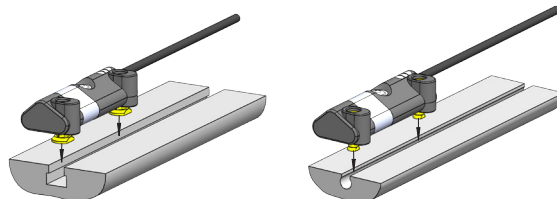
Установка пазовых сухарей в паз (Т-образный паз на рис. слева, С-образный паз справа)
